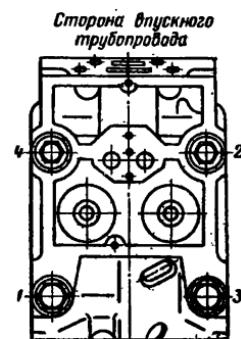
Порядок затяжки болтов крепления головки цилиндра
